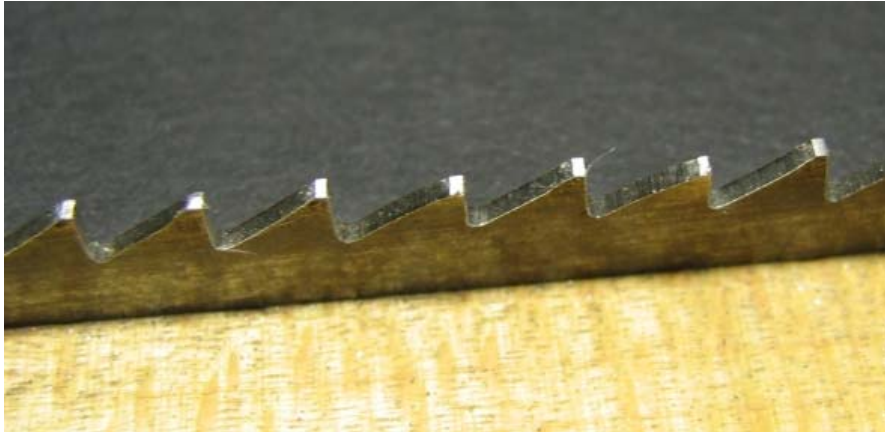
Zähne einer Längsschnittverzahnung mit Kopfflächen vor dem Ausfeilen (im hölzernen Sägefeilkloben, die hintere Backe ist zur besseren Sichtbarkeit im Foto durch dunkles Papier abgedeckt)
